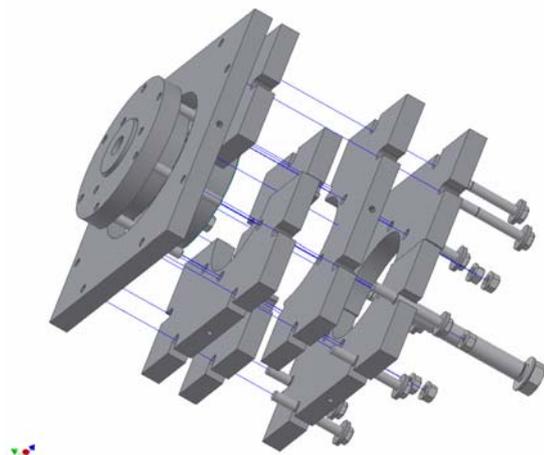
Durch die Zusammenstellung kleiner Einzelbauteile mit geringem Gewicht, lassen sich die Tilger auch an schwer zugänglichen Orten ohne Hebezeug montieren
